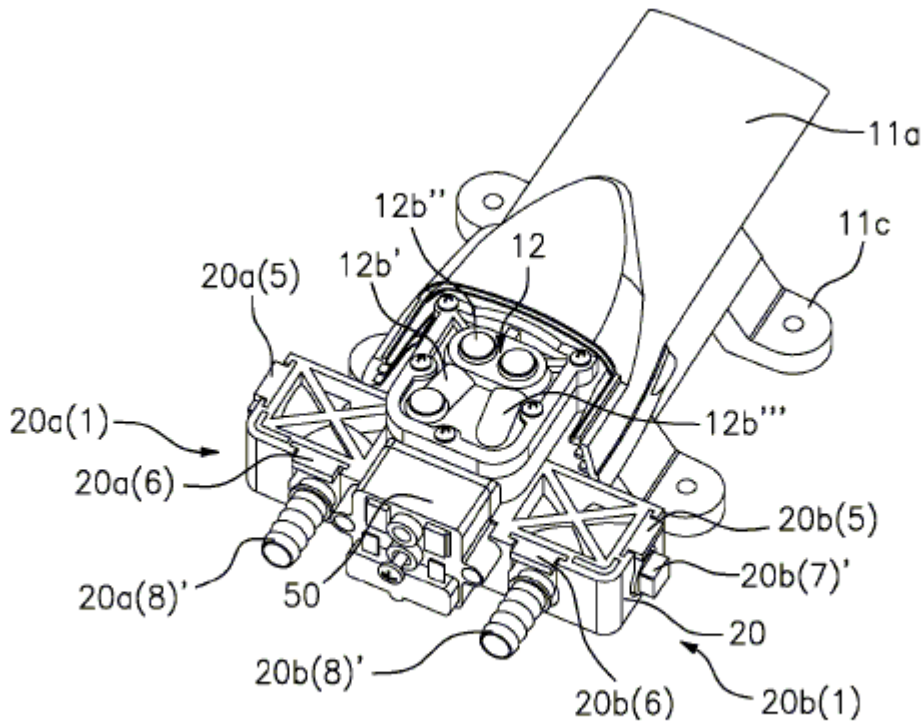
B: Conjunto de bomba que presenta otro tipo de conexión de accesorio de puerto en la parte frontal
